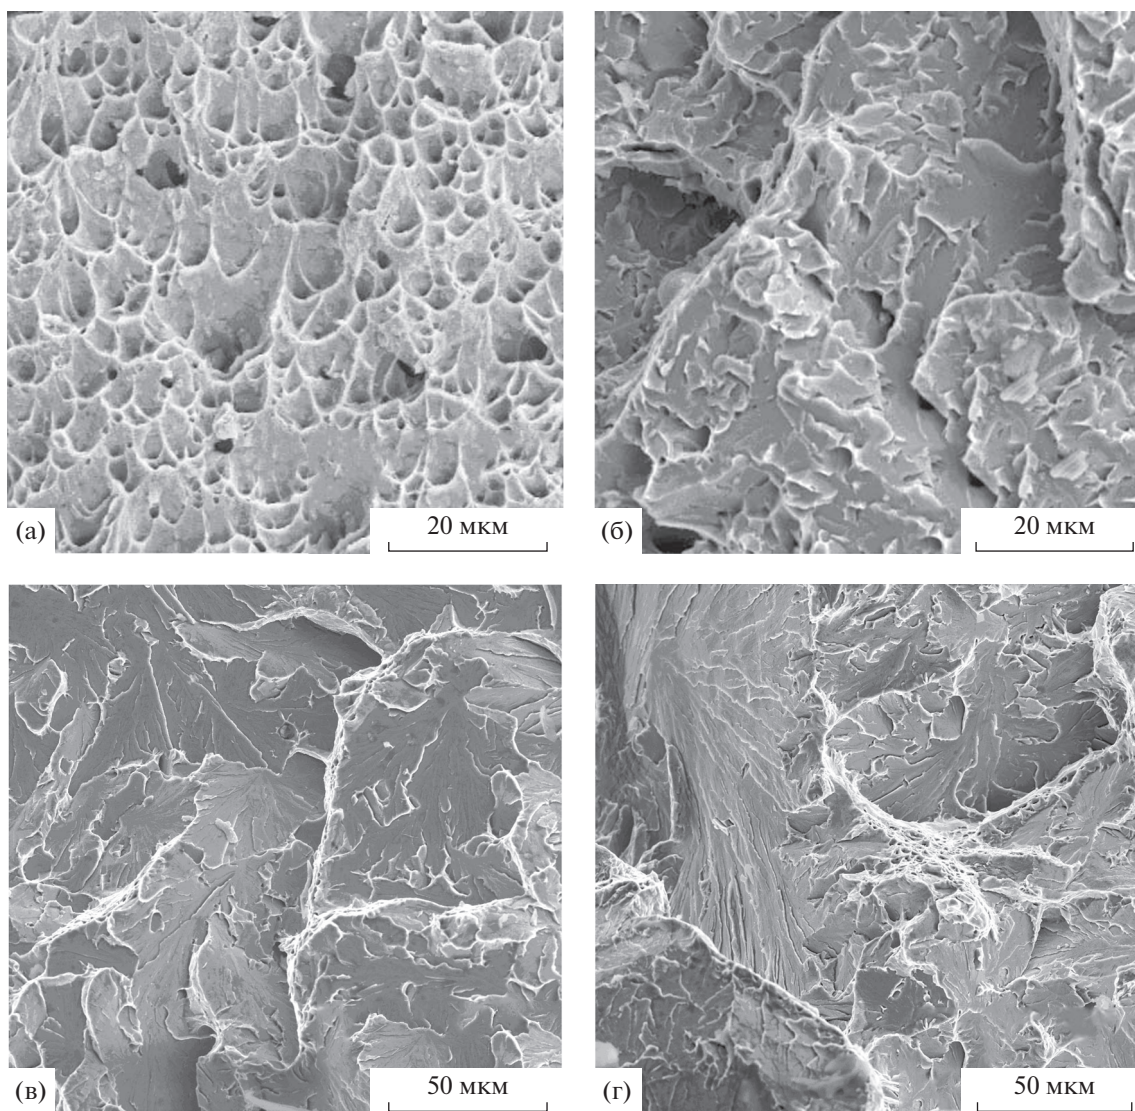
Фрактограммы изломов образцов сварных соединений с надрезом по металлу шва (а, б) и линии сплавления шва ДСФ (в, г): а, в – область зарождения трещины; б, г – область развития трещины.
